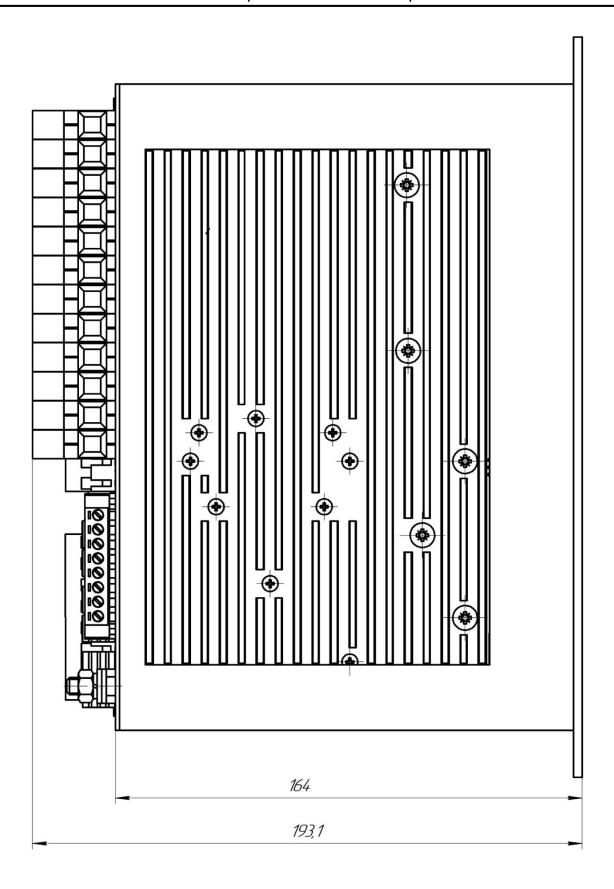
Габаритные размеры устройств РЗЛ-05.Ф5, РЗЛ-05.Ф6. Вид сбоку
